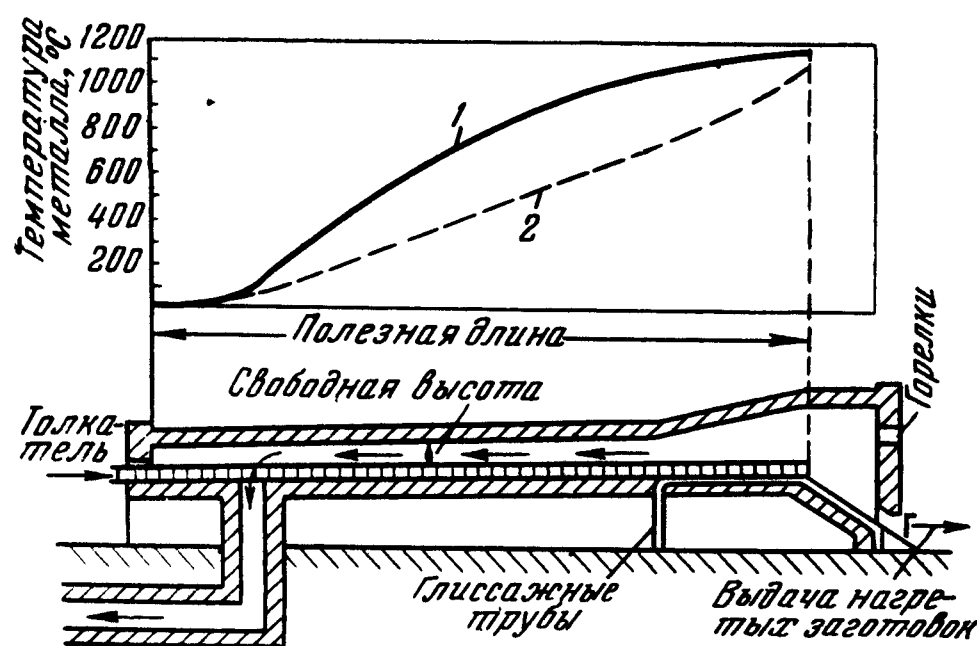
Схема методической печи для одностороннего нагрева тонких заготовок.
